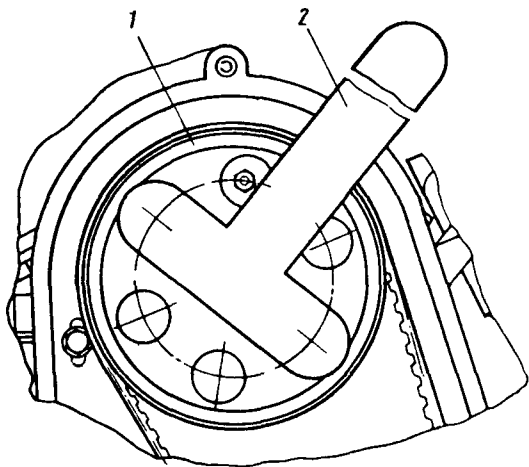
Проворачивание двигателя за шкив распределительного вала при регулировке зазоров в клапанном механизме:
